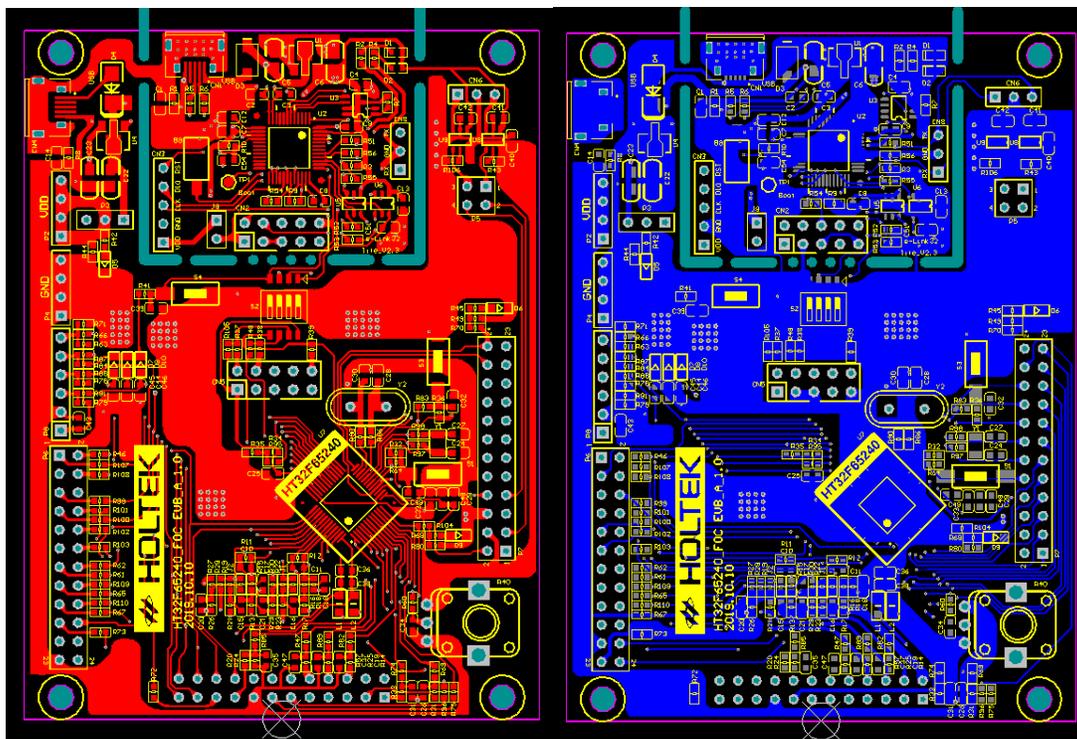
直流無刷馬達開發平台 FOC-EVB PCB Layout: (a) 上層; (b) 下層
